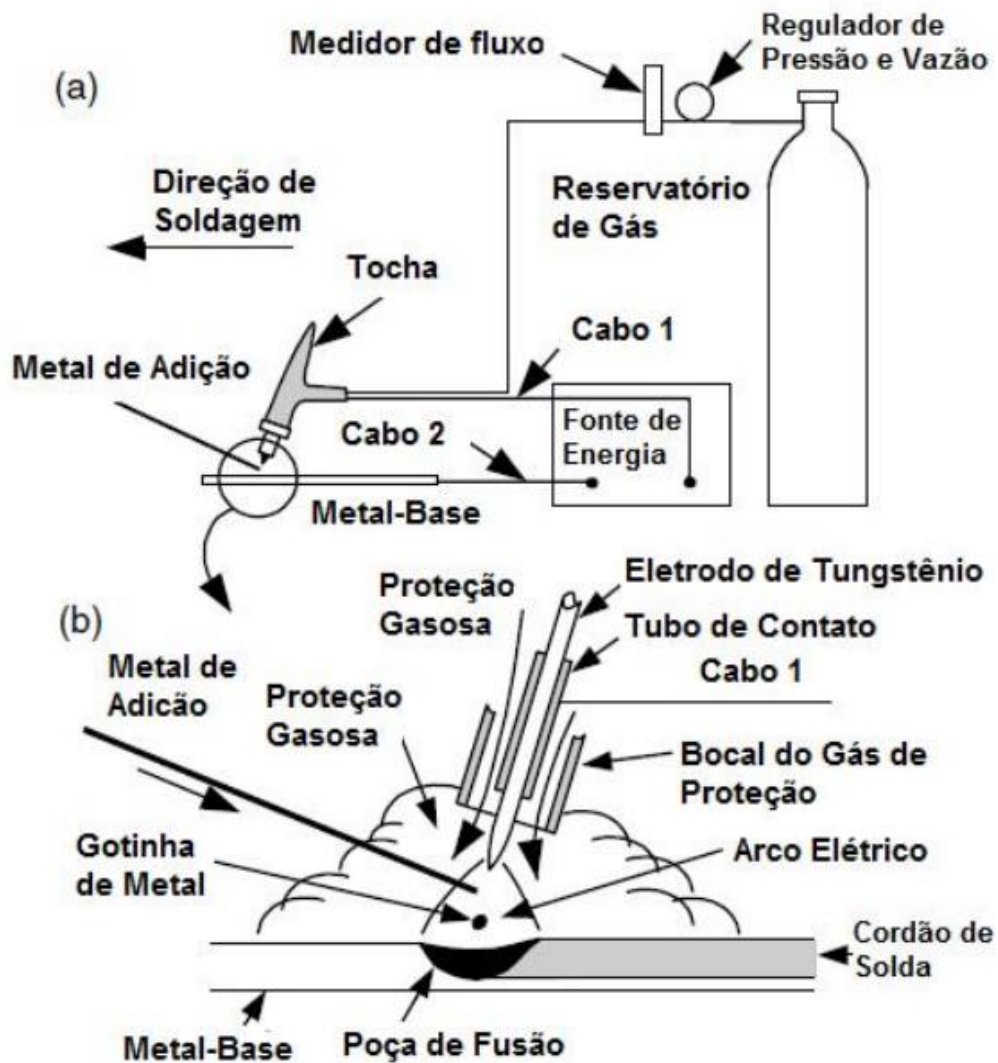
Soldagem GTAW: (a) Equipamentos GTAW; (b) Vista frontal da soldagem [30]
